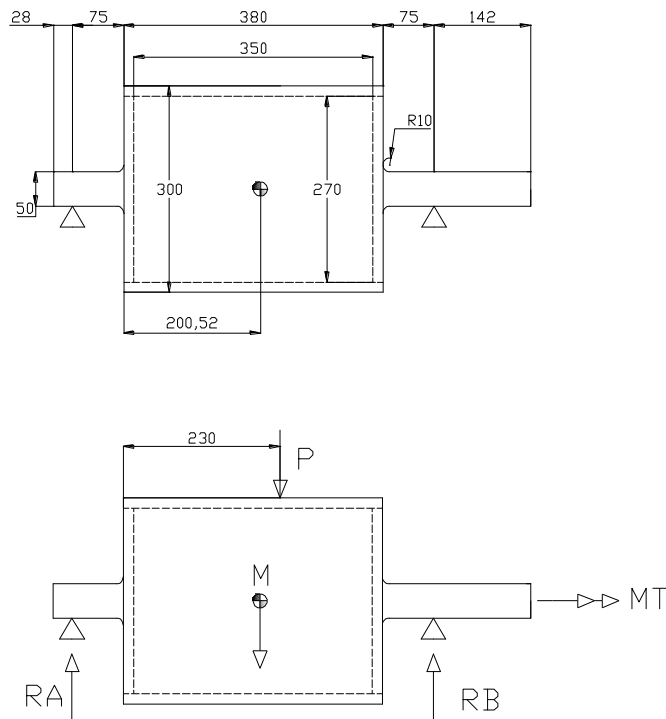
3: Esquema del rodillo con dimensiones (mm) y cargas actuantes
